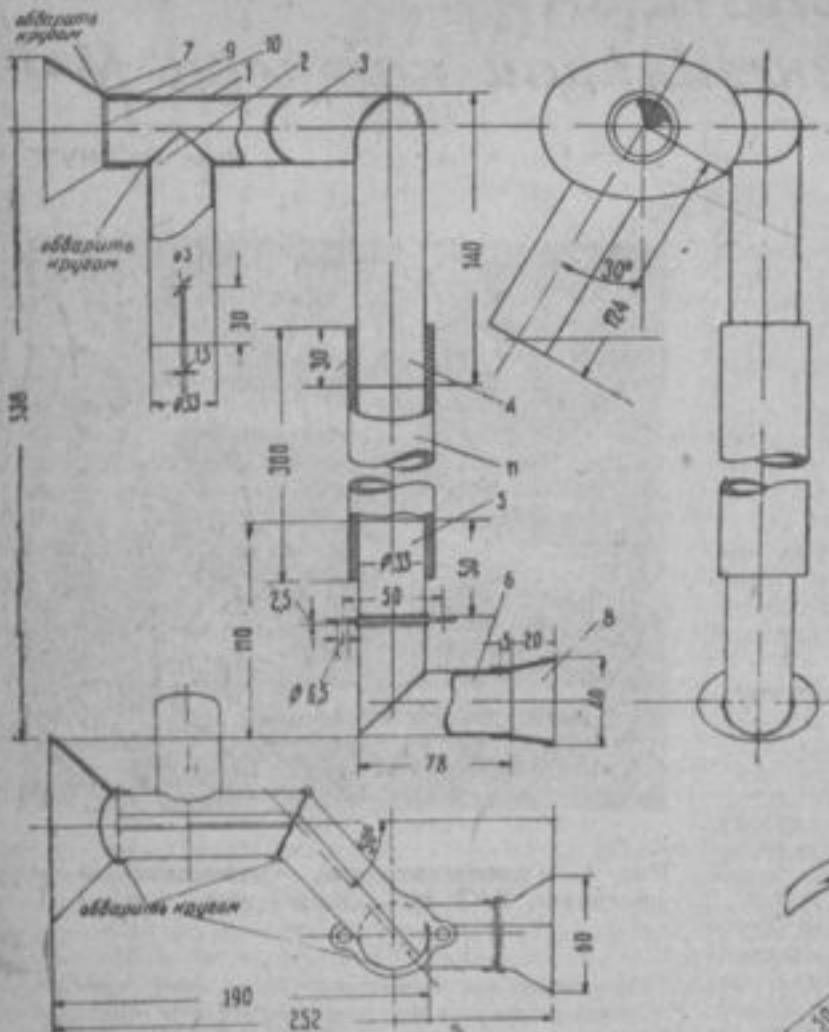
Схема газо-поглотителя для машин М-1, ГАЗ-А и АА
